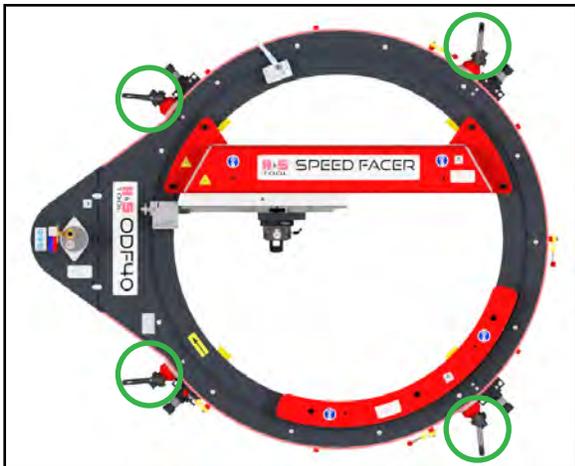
POINTS DE LEVAGE (MACHINE ODF40)
